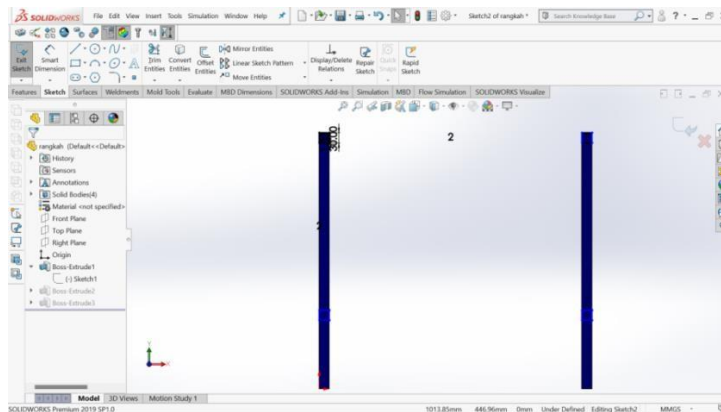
Desain 2 Dimensi Besi Hollow
